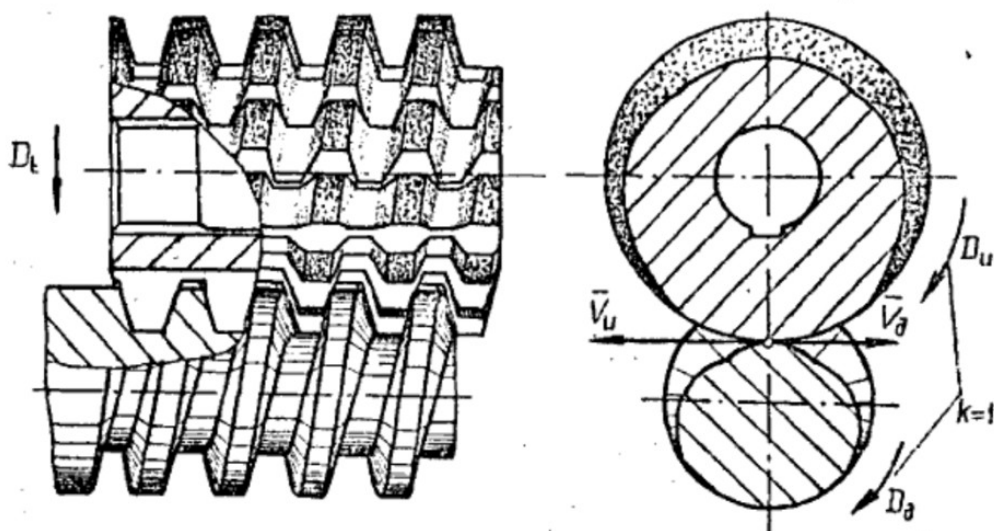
Способ формообразования резьбы при синхронном вращении заготовки и винтового инструмента [18]
